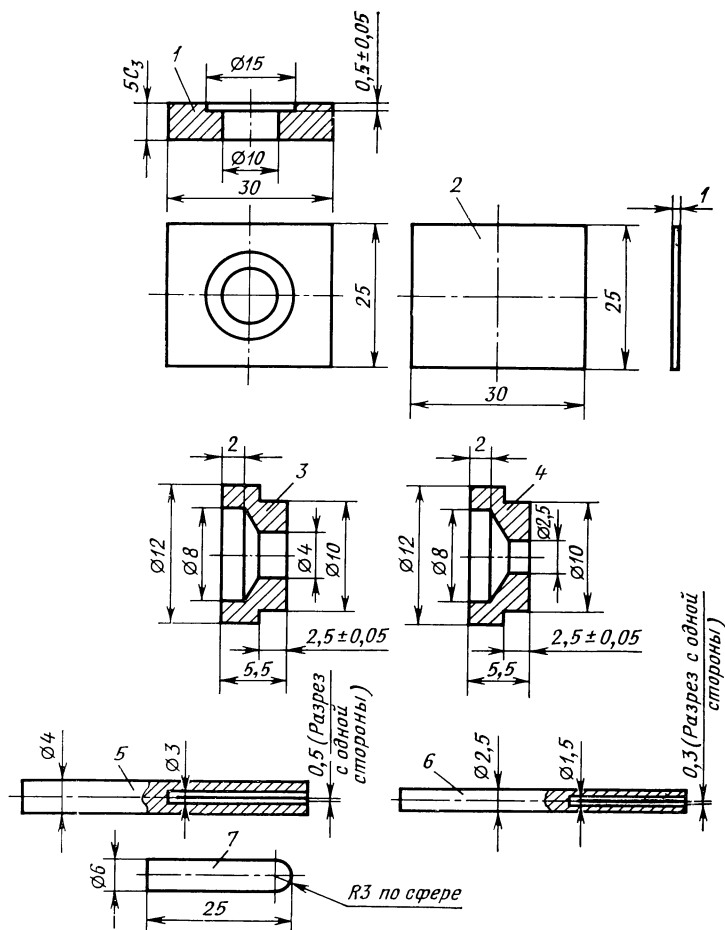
Приспособления и инструмент для сверления отверстий в кварцевых пластинах:
